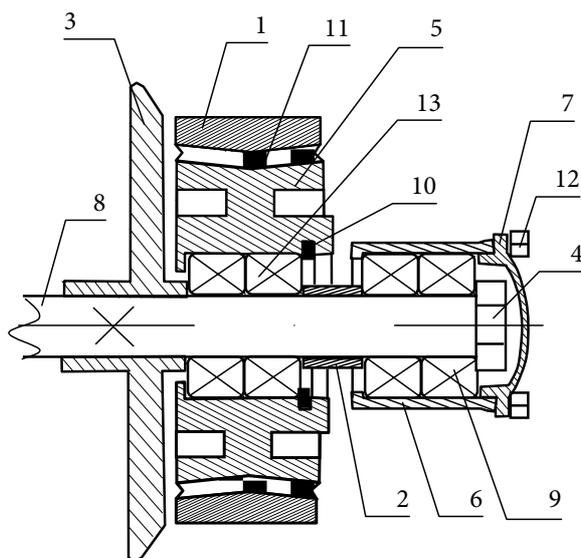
Новая конструкция колеса колесной пары рельсового транспортного средства
